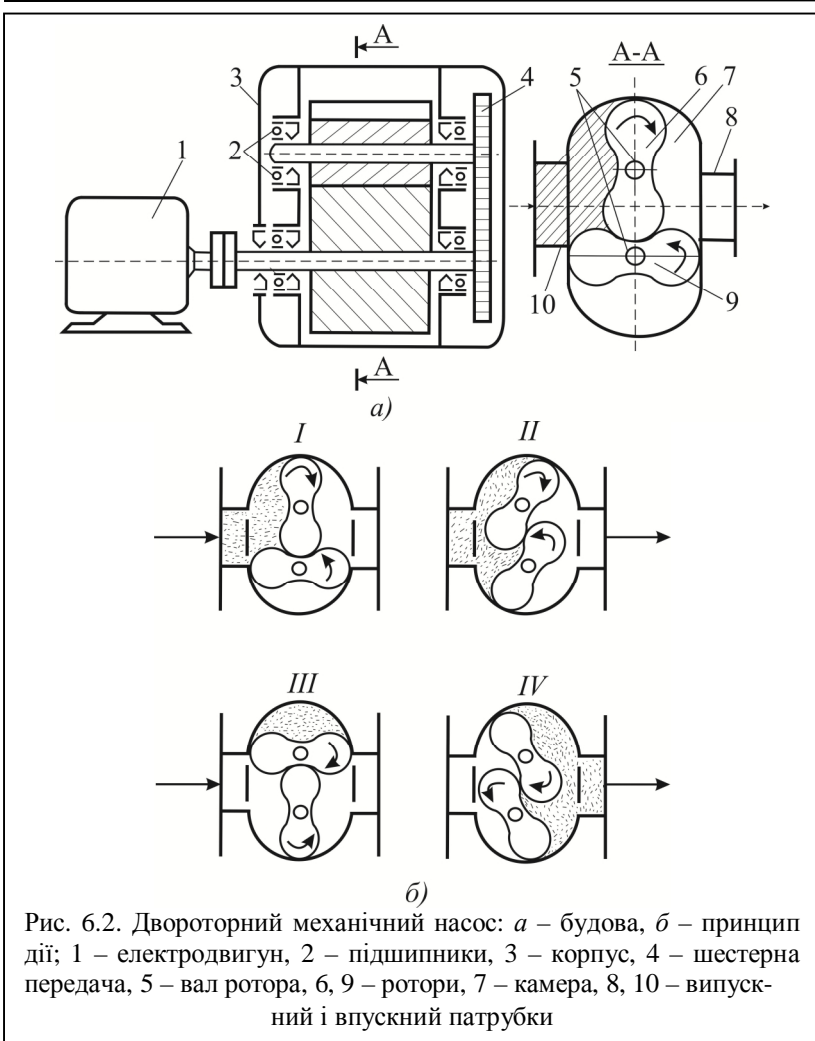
Двороторний механічний насос: *а* – будова, *б* – принцип дії; 1 – електродвигун, 2 – підшипники, 3 – корпус, 4 – шестерна передача, 5 – вал ротора, 6, 9 – ротори, 7 – камера, 8, 10 – випускний і впускний патрубки
